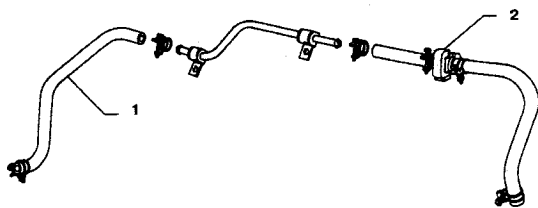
Вакуумный шланг и обратный клапан (См. Раздел 13)
